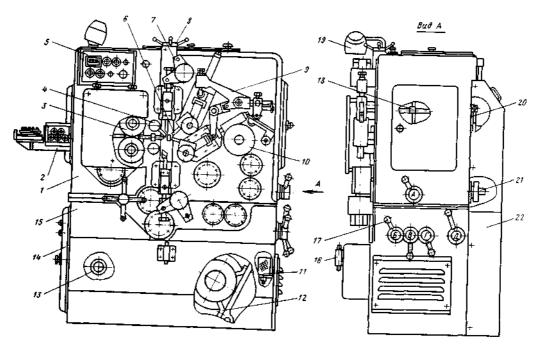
Типовая конструкция автомата для холодной навивки пружин (муфтного вида):
